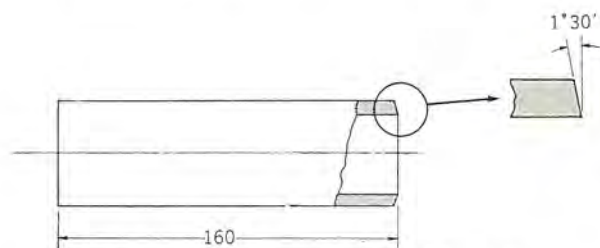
パイラ加工図 Fig. 3.3 Work piece.
